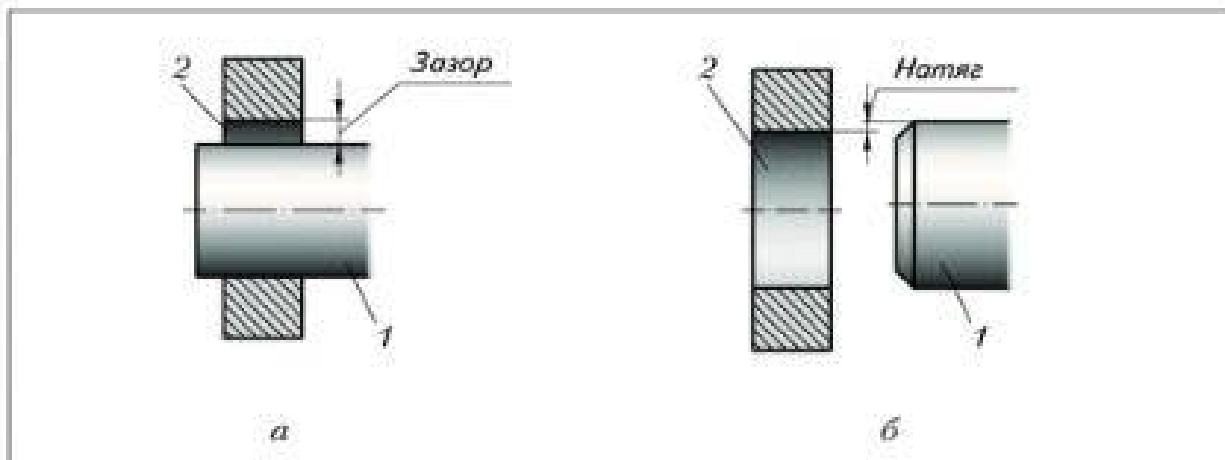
Посадка вала в отверстие: *a* – с зазором; *b* – с натягом: 1 – вал; 2 – отверстие
